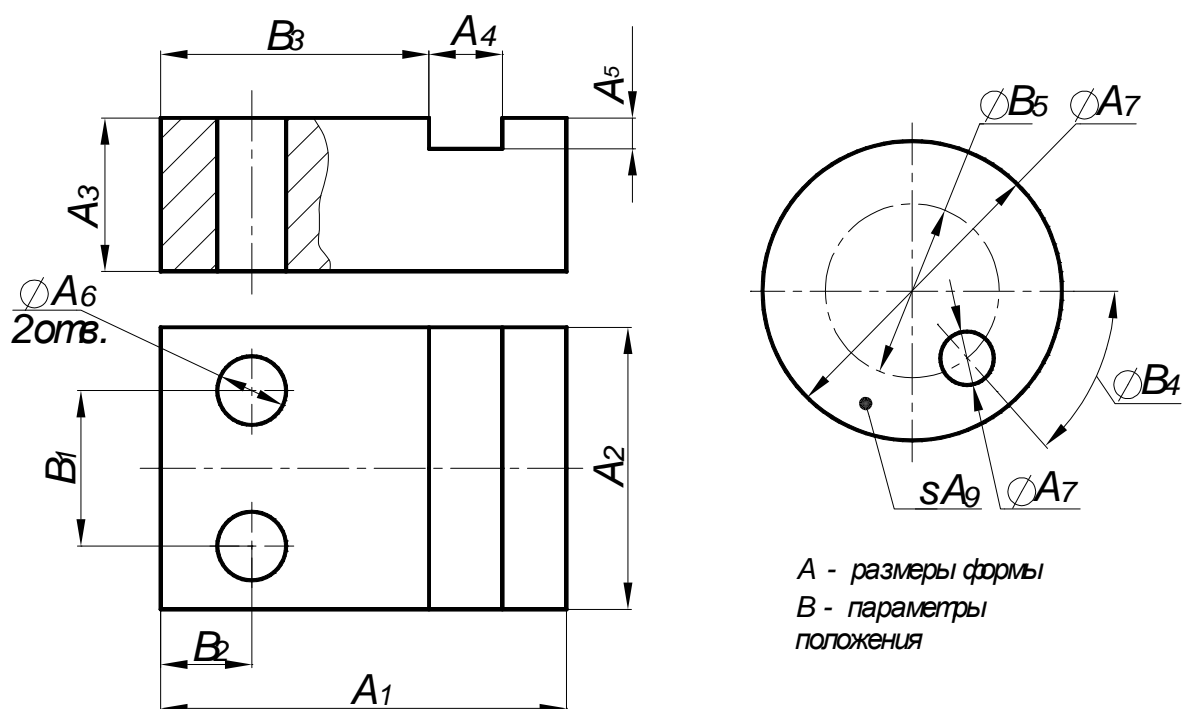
Чертежи деталей с простановкой размеров форм и размеров положений
